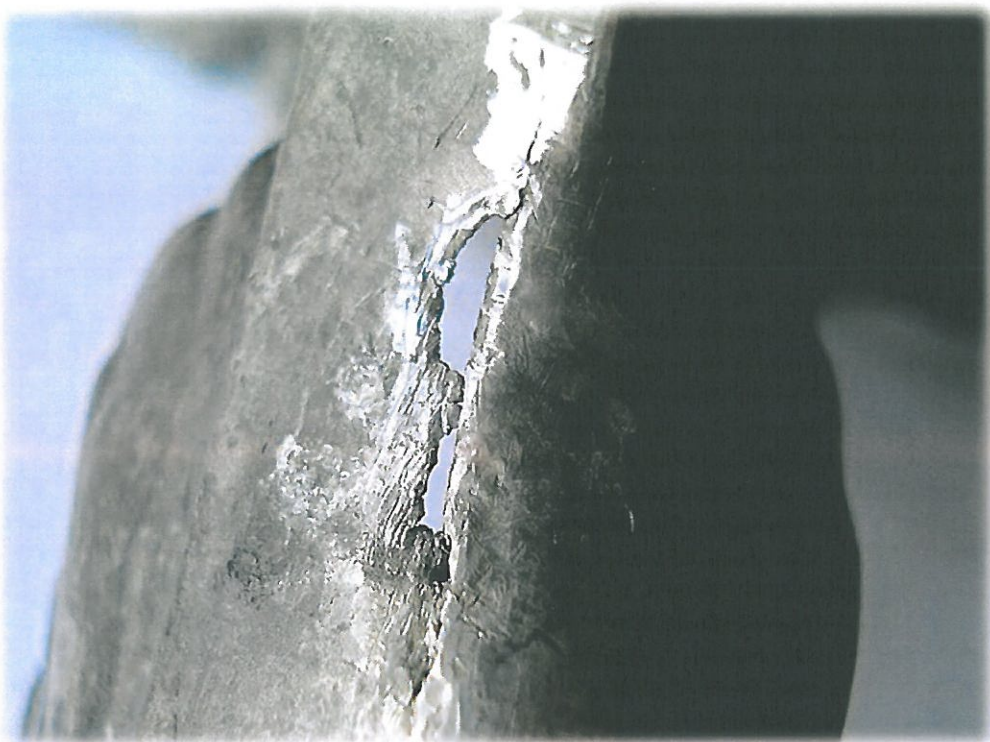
Místa po zapájení. Horní prasklina je již začištěna
